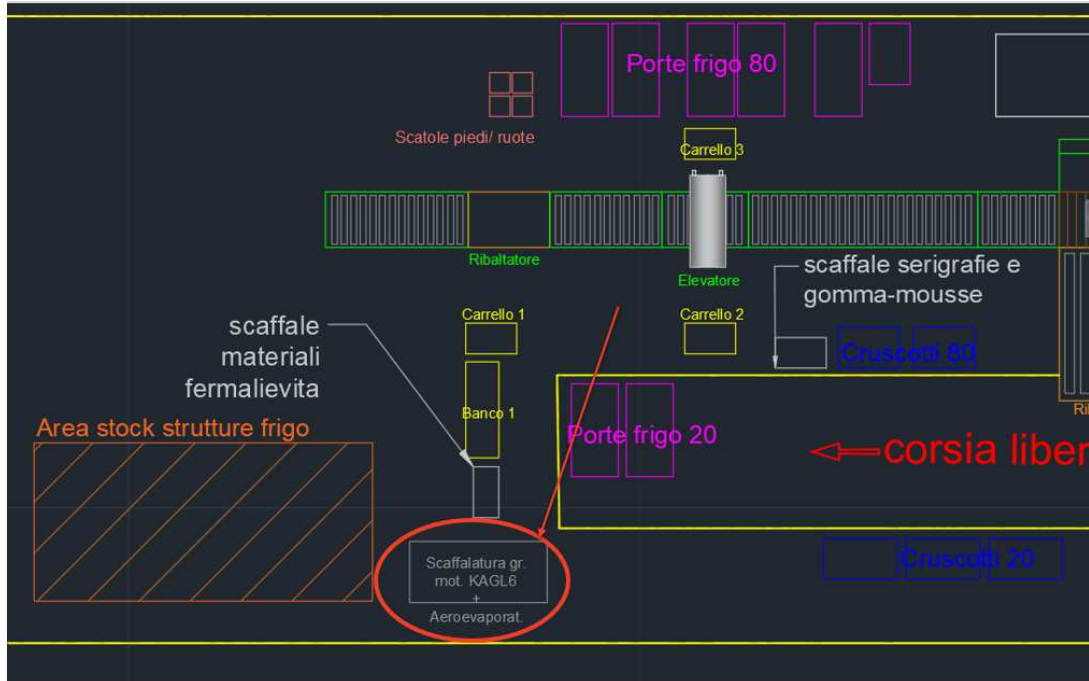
Posizionamento scaffalatura su layout di prima stazione
